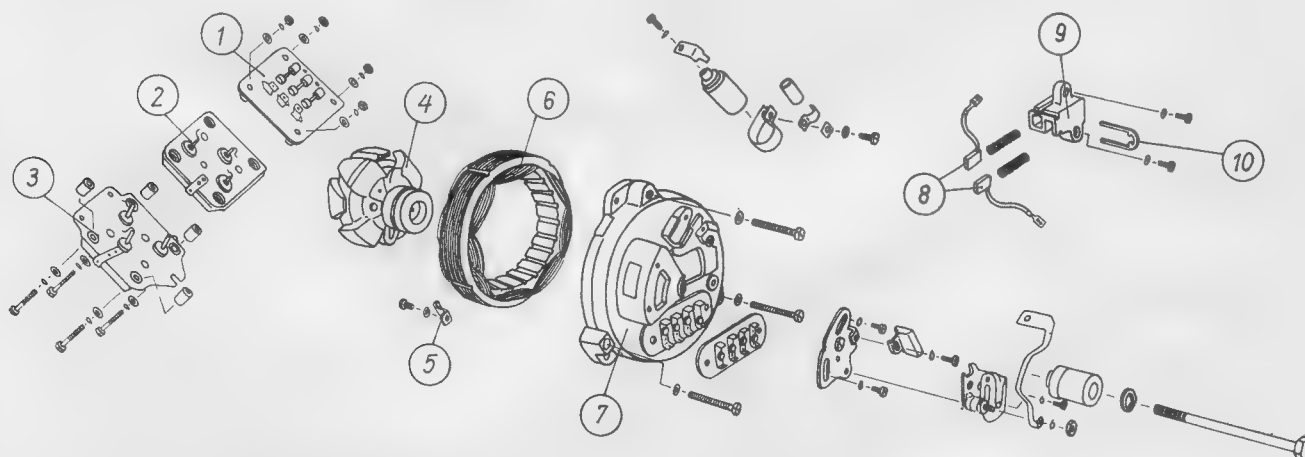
Explosivdarstellung der Drehstromlichtmaschine
